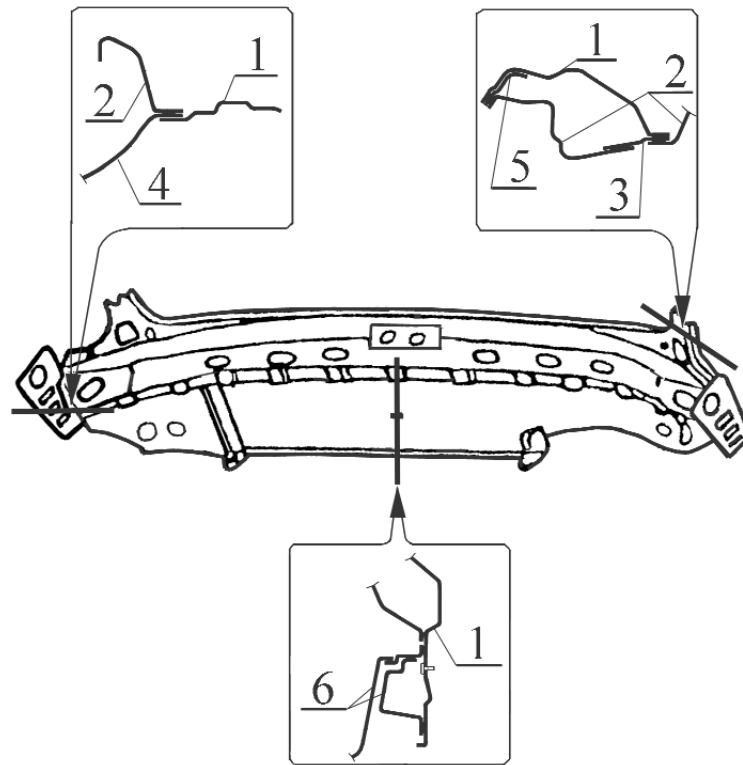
Соединение панели задка с поперечиной в сборе 1119-5601080 с сопрягаемыми деталями. Количество сварочных точек по таблице 17.
